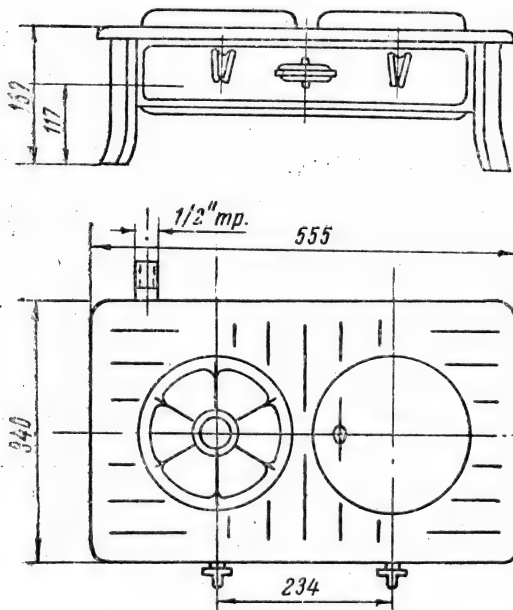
Внешний вид и габаритные размеры плиты (тагана) типа ПГ-2В.
